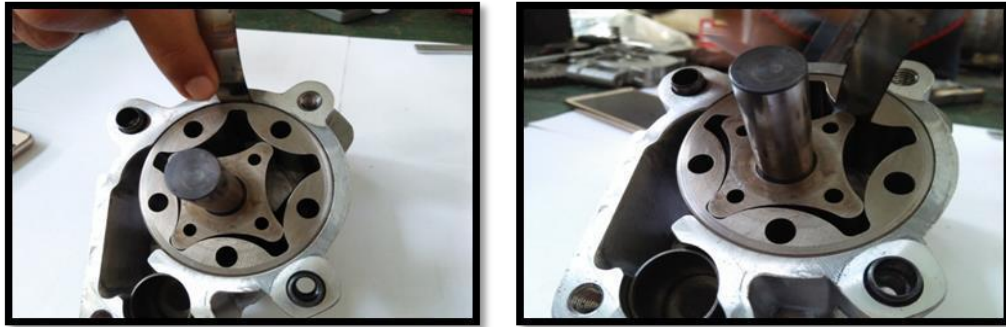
19 Pengukuran *Depth of the bore for the gear
